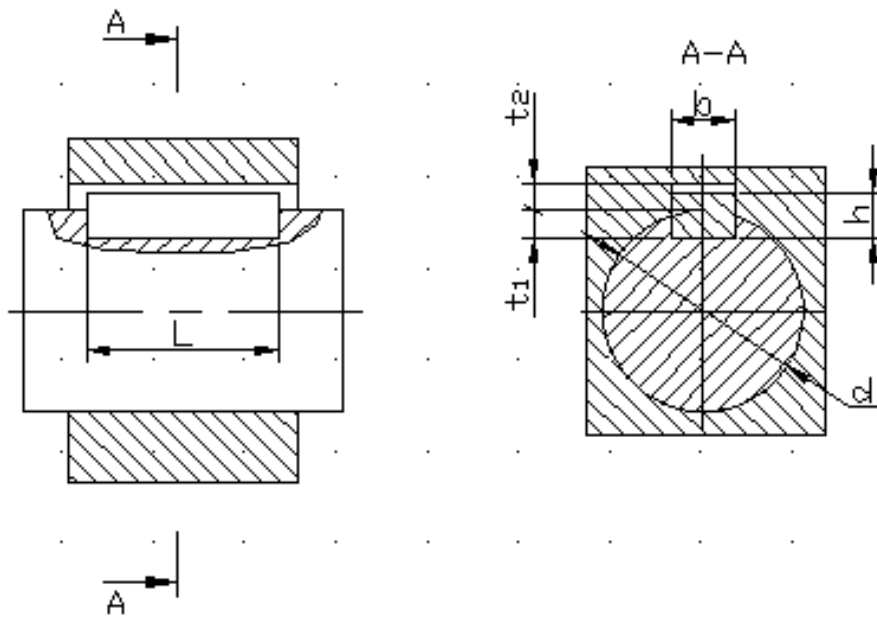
Основные конструктивные размеры для шпоночных паза и канавки
